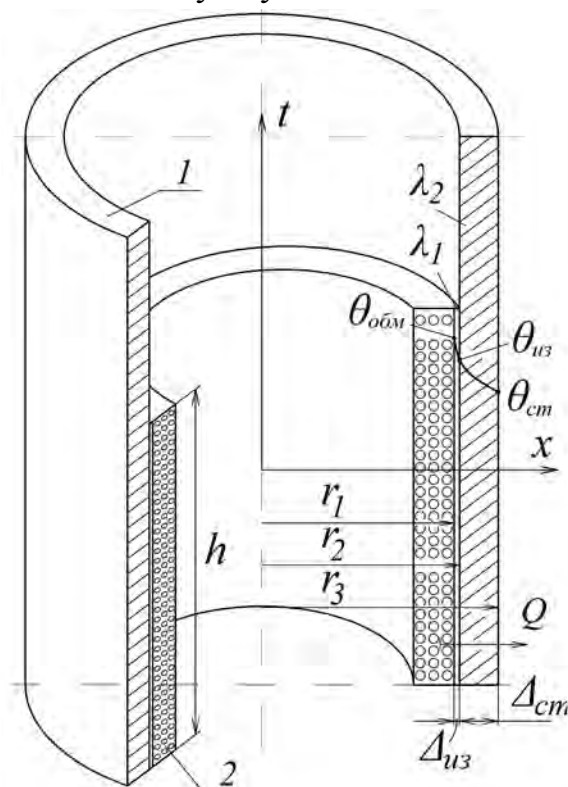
Эскиз корпуса ЛЭМД без воздушных зазоров
